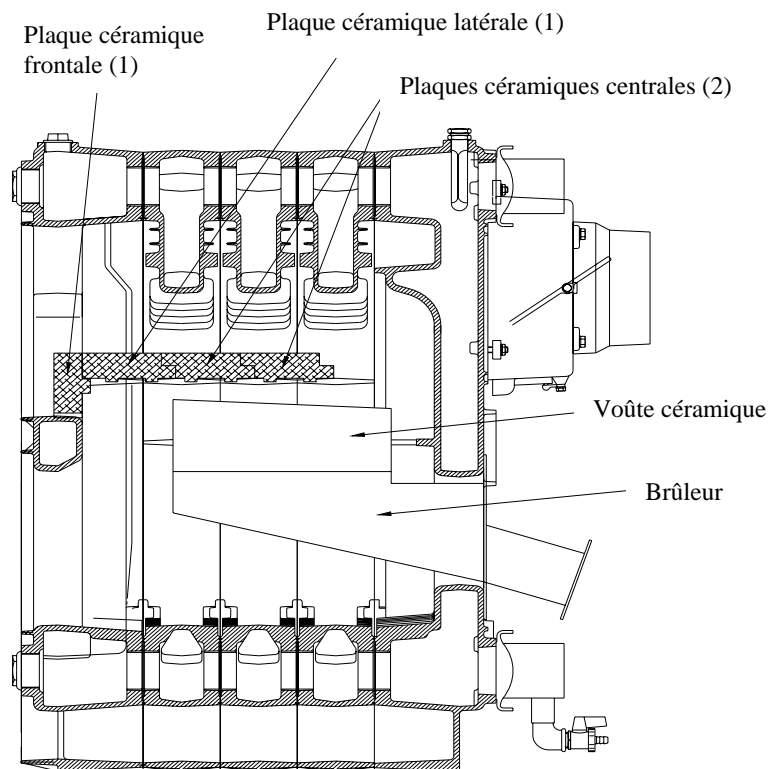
Emplacement des plaques céramiques dans un corps de chaudière à 5 éléments
